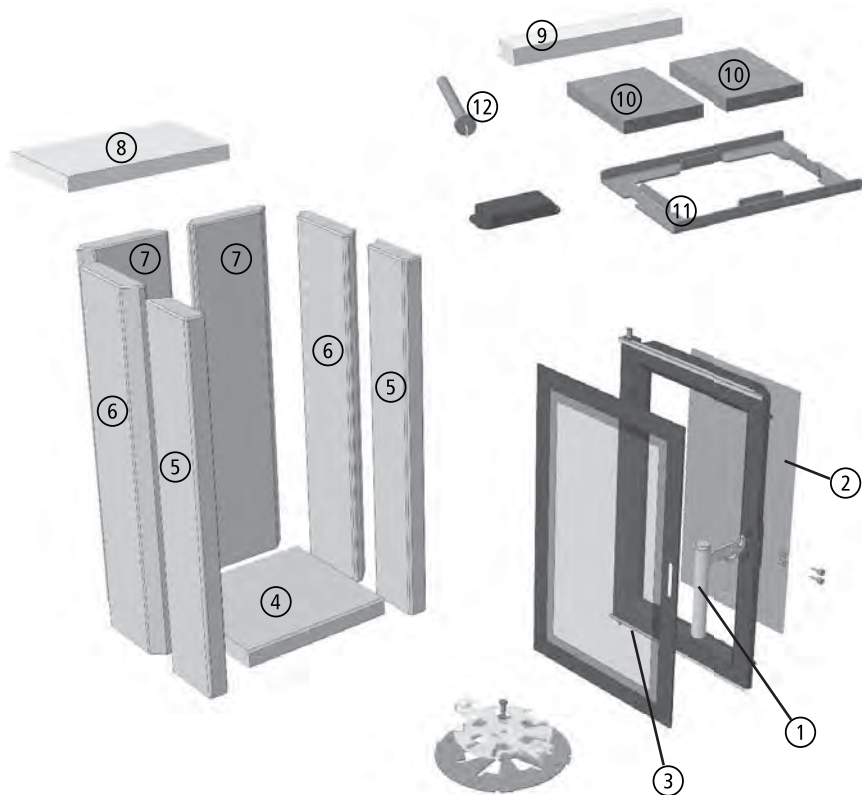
Aperçu des pièces de rechange du CORNA tec
